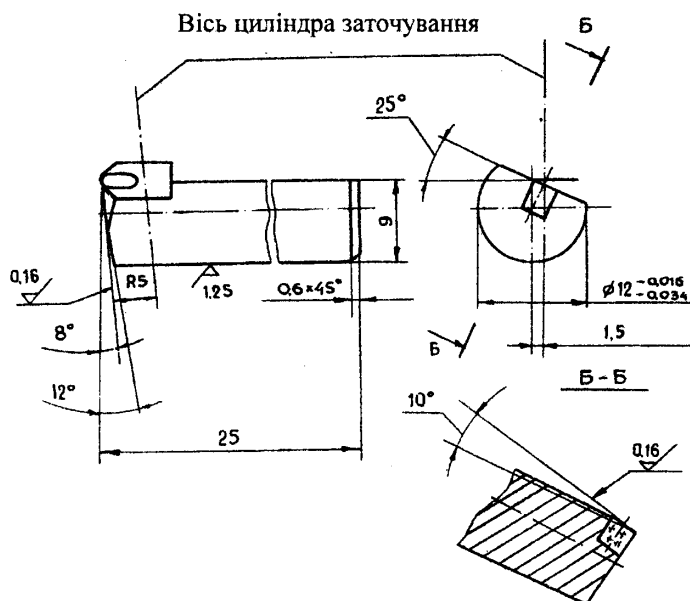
Конструкція різального ножа фрези косокутного різання
